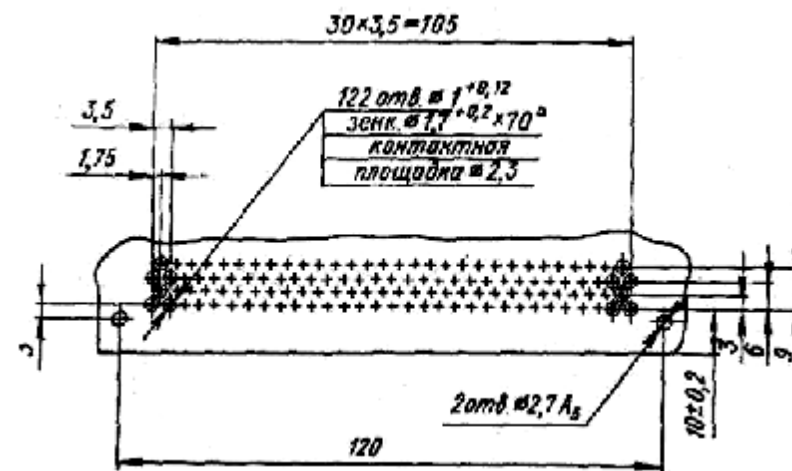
Разметка посадочного места для вилки разъёма ГРПМ1-122ШУ на печатной плате
